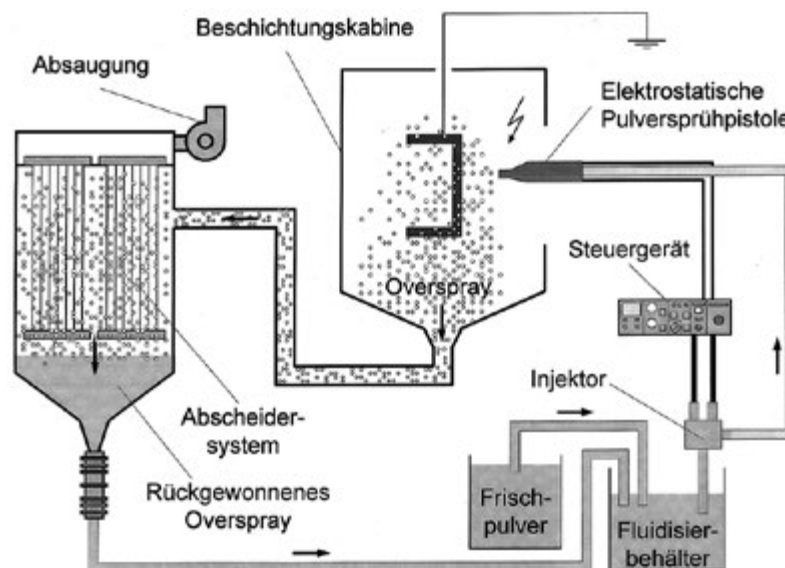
Aufbau einer elektrostatischen Pulverbeschichtungsanlage
